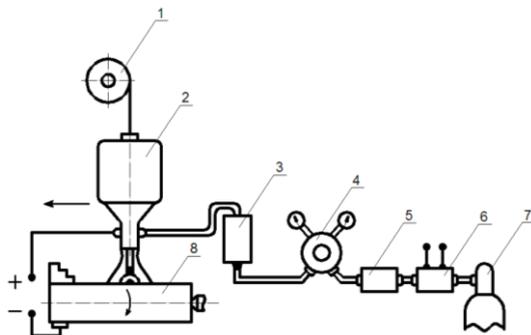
Схема установки для дуговой наплавки в углекислом газе:
